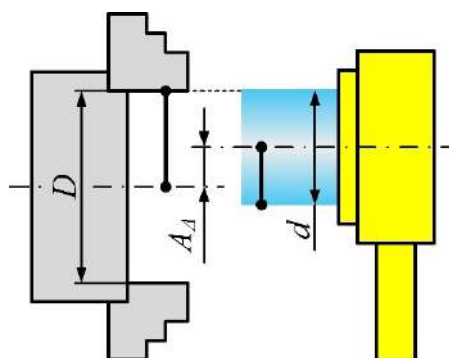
Встановлення заготовки у самоцентруючий патрон верстата
